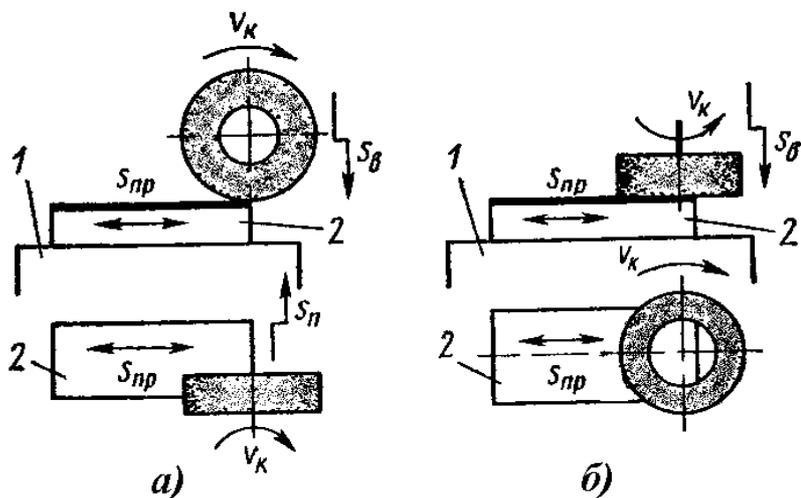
Схемы обработки заготовок плоским шлифованием: а – периферией круга; б – торцом круга; 1 – стол станка; 2 – обрабатываемая деталь
